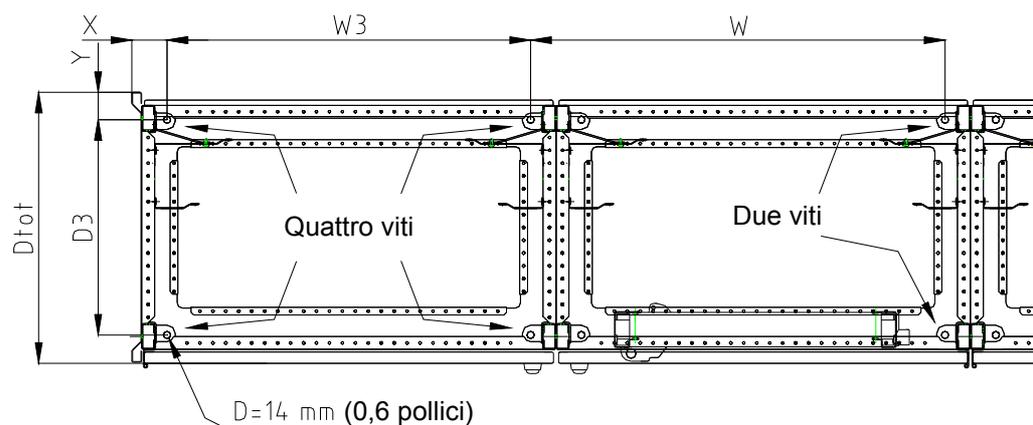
Posizioni dei fori per il fissaggio degli armadi a pavimento
